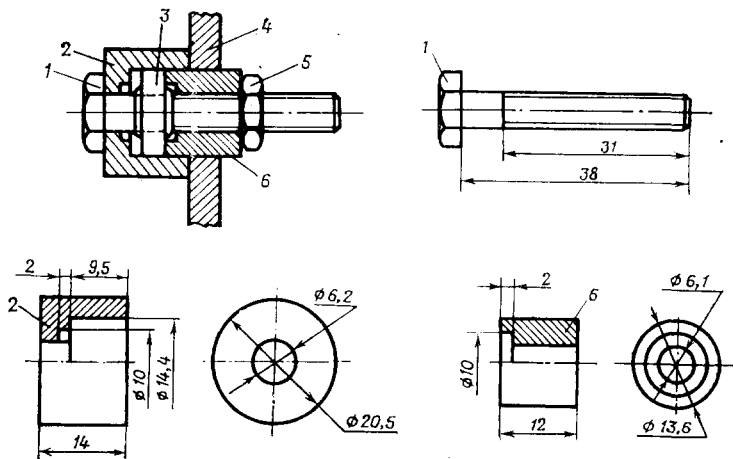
Приспособление для выпрессовки подшипников Ш-6, ПС-6 из качалок и поводков в системе управления двигателем:
